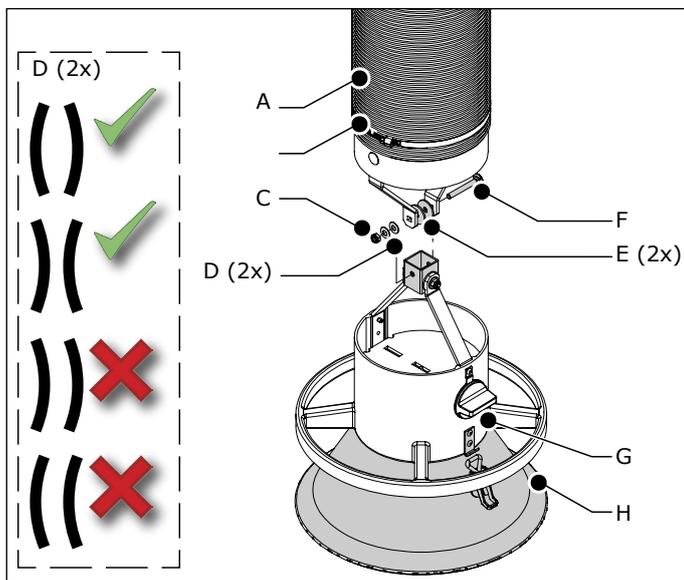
Montaje de la campana (brazo de tubo metálico)
